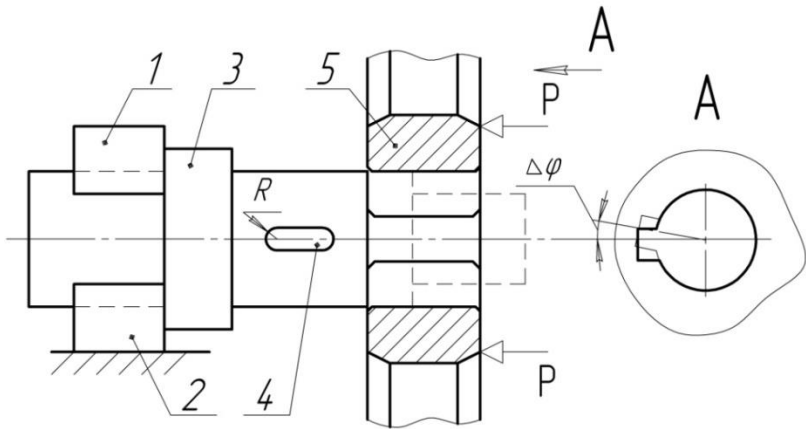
Схема установлення зубчастого колеса на валу:
